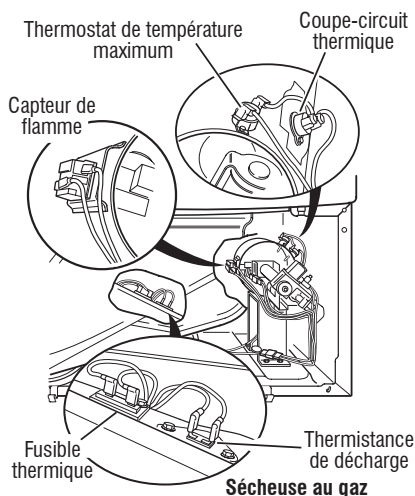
Composants thermiques, sècheuse au gaz, vue de face.
